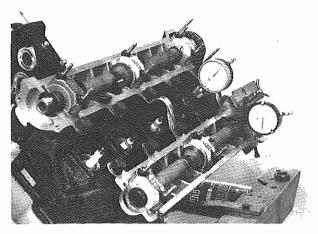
Montare il comparatore n. 42 Fit gauge No. 42
